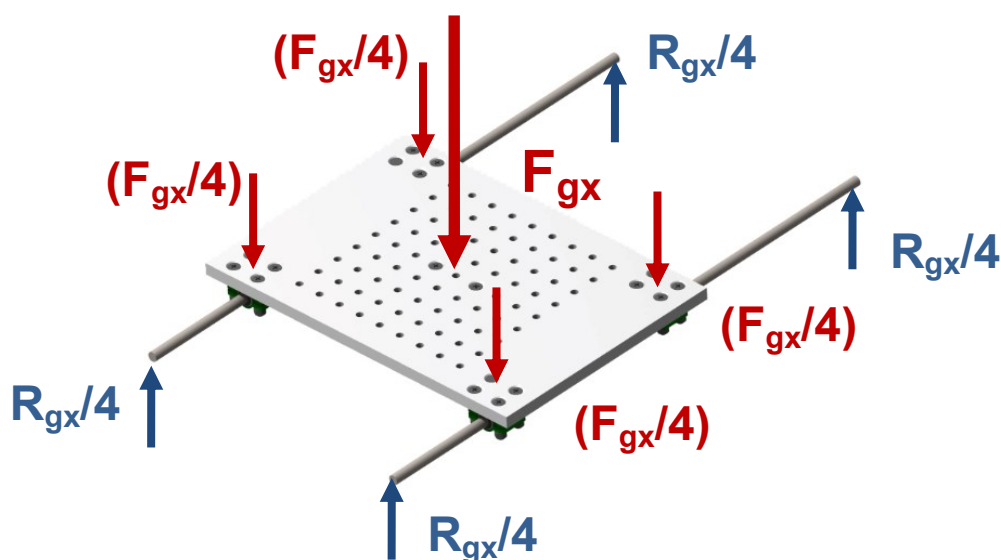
Zobrazení rozboru zatěžujících síly na celý CNC stroj
